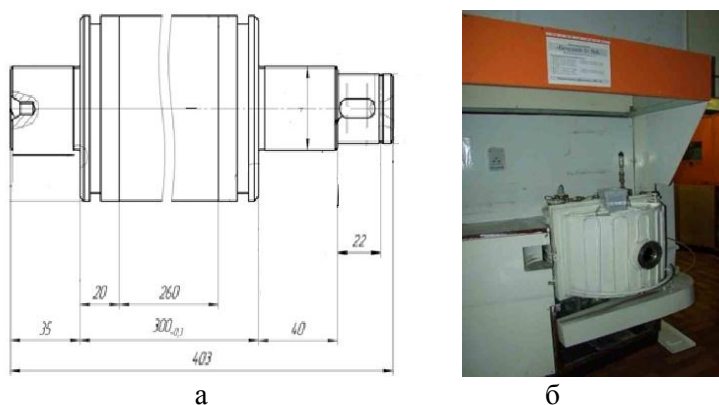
а- валок из стали 45 и предназначенный для листовой прокатки изделий из тугоплавких металлов и их сплавов; б- установка ионно-лучевого легирования «Везувий-5» (вид со стороны приёмной камеры)
